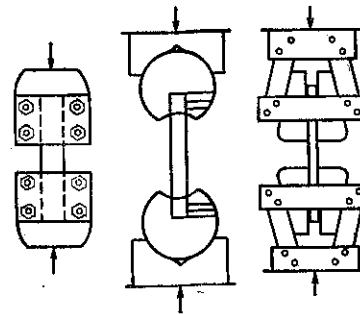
Конструкции захватов для испытаний образцов на сжатие [38].
